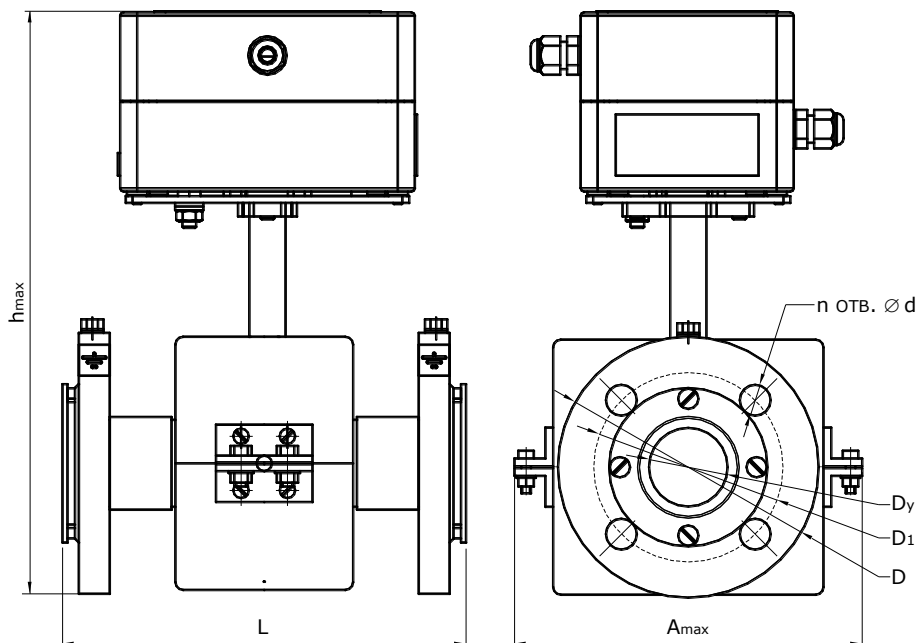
Габаритные и установочные размеры ПРП
